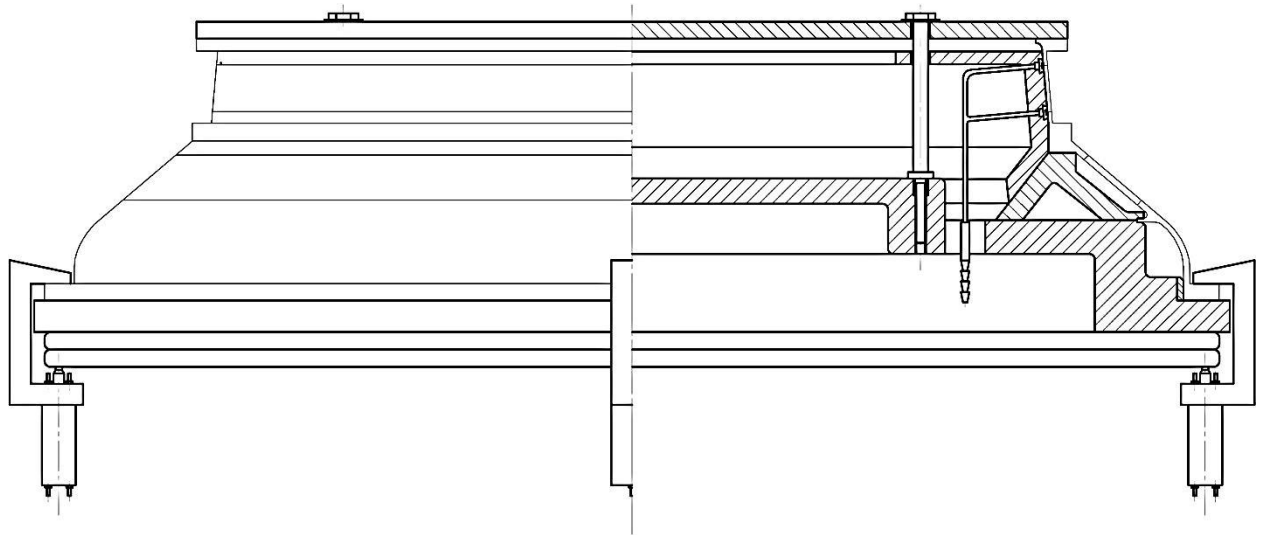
Пристосування для зварювання корпусу ЦПК
